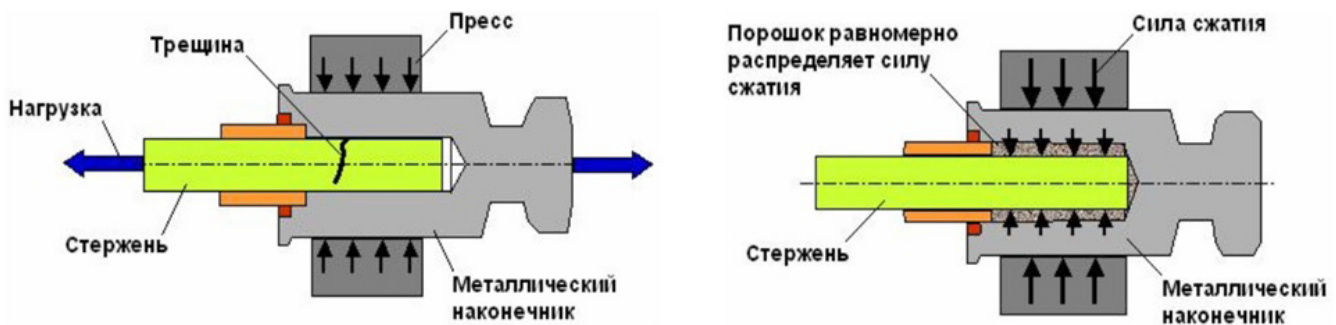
Процесс опрессовки металлического оконцевателя: а) – традиционный способ, б) – предлагаемый способ
